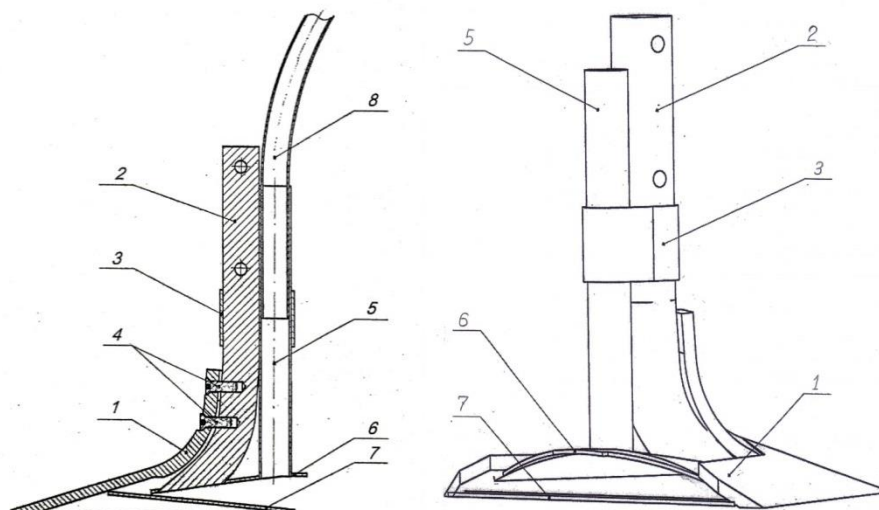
Рабочий орган для культивации и разбросного посева зерна по стерне, модернизированный от культиватора КФГ-3,6
